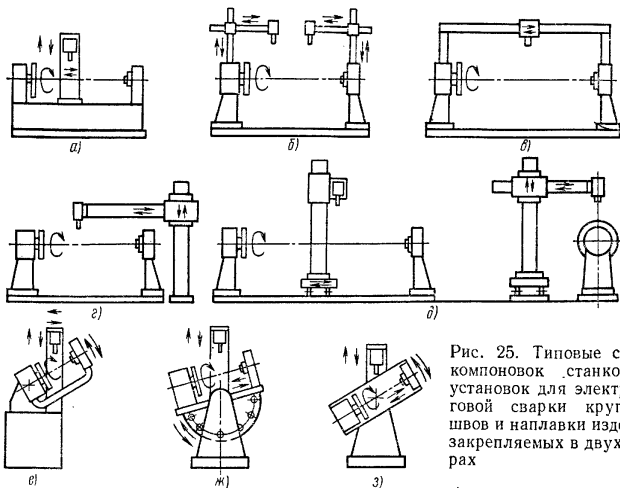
Типовые схемы компоновок станков и установок для электродуговой сварки круговых швов и наплавки изделий, закрепляемых в двух опорах
